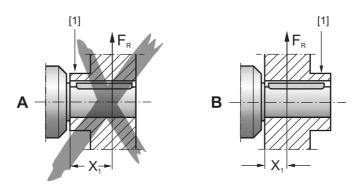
Disposição de montagem correcta de uma polia ou roda dentada
